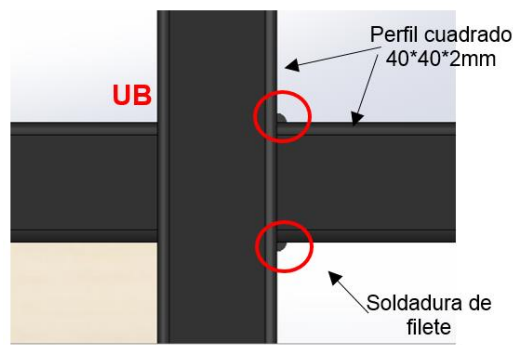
Vista superior de la junta soldada en el punto UB. Elaborado por: Castillo J, y Obando R (2018).
